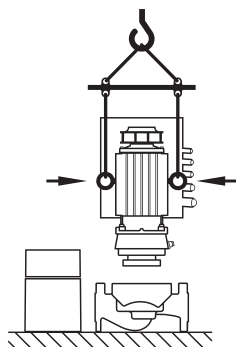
Transportul ansamblului motor cu rotor hidraulic
